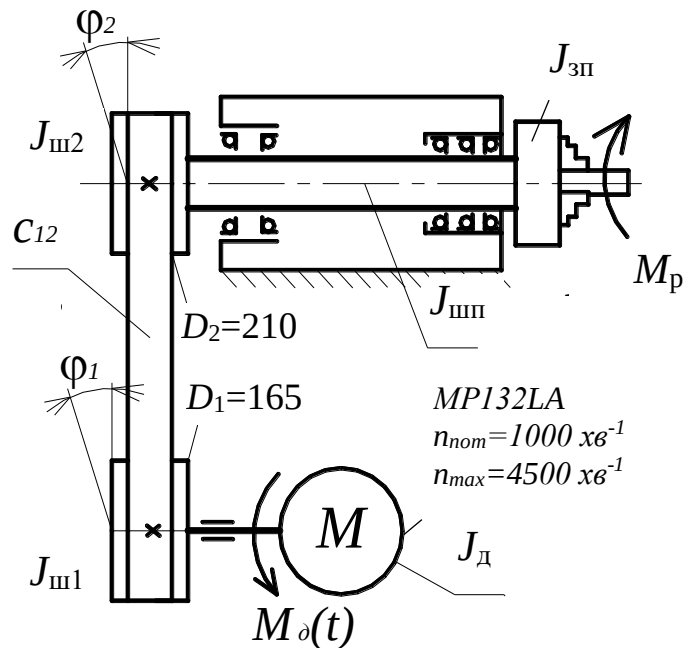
Конструктивна схема приводу головного руху токарно-револьверного верстату з ЧПК
